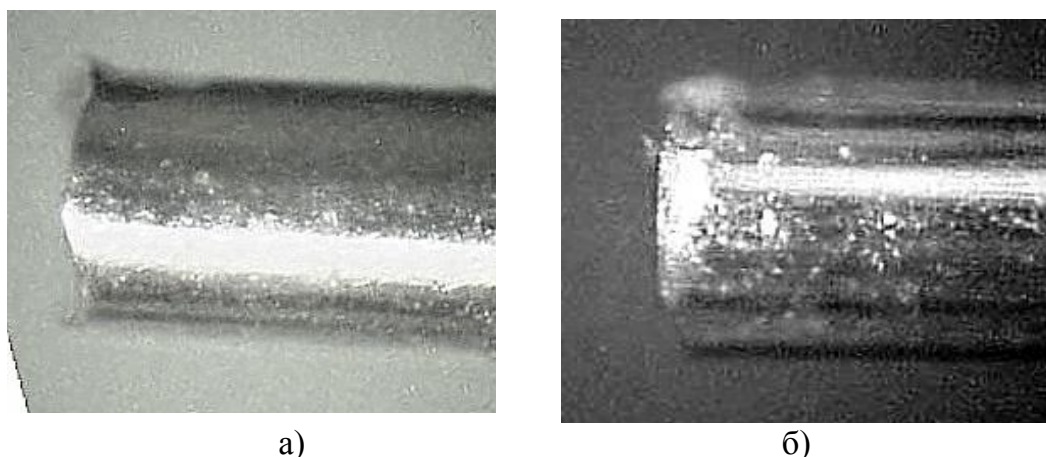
Режущая часть иглы из нержавеющей стали (увеличение $\times 60$):
